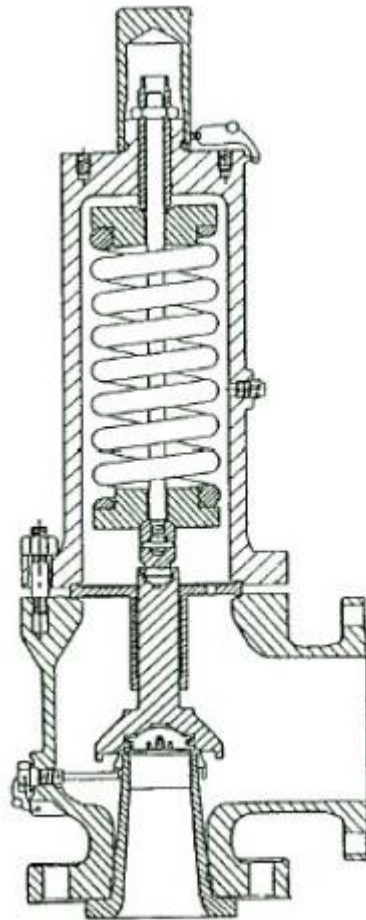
Válvula de Seguridad equilibrada de Pistón (Crosby Valve & Eng. CO.).
